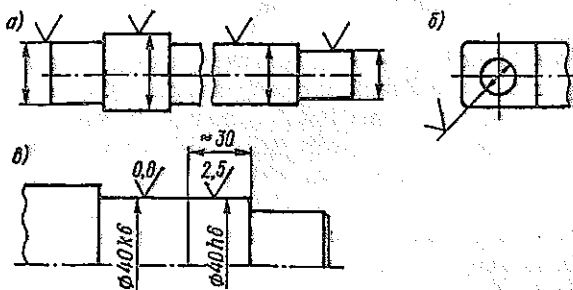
Расположение знаков шероховатости на изображении детали
